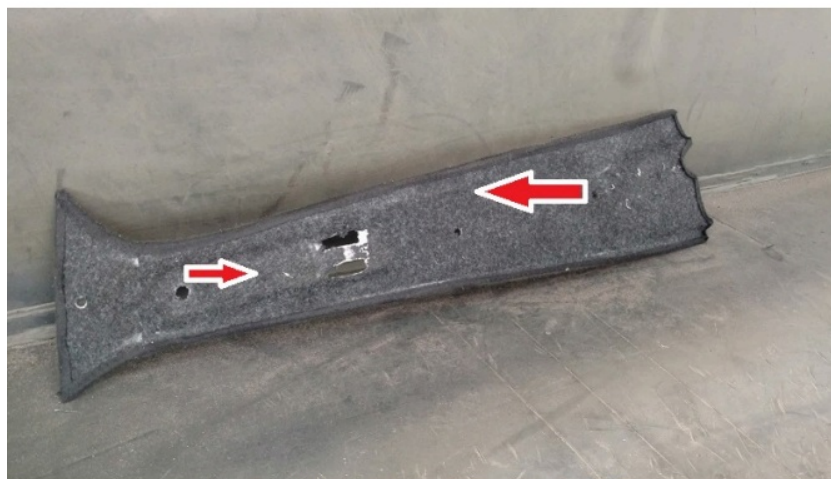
Detalhe do carpete aplicado na face oposta da chapa de aço
